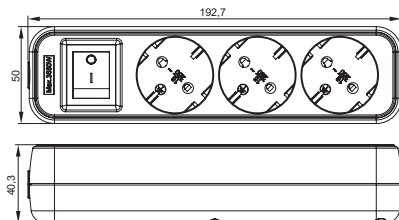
Габаритные размеры удлинителей (лист 1 из 4) / Figure 1 – Overall dimensions
